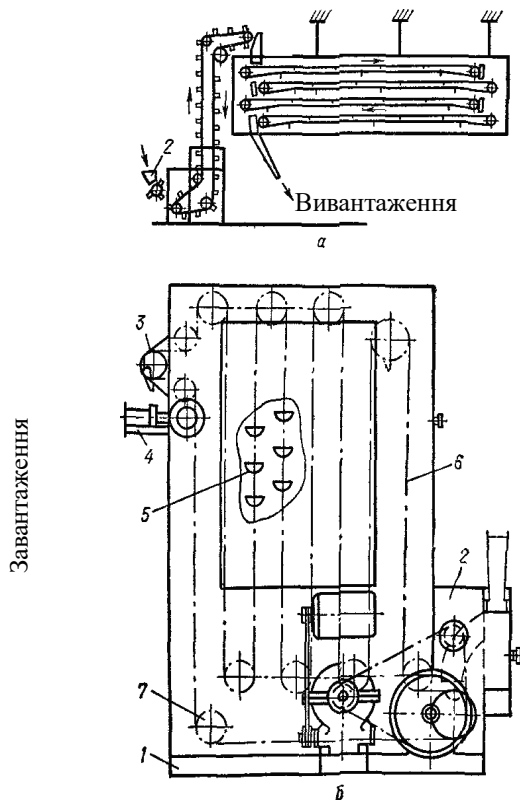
Шафи попереднього вистоювання: а – стрічкова; б – коліскова шафа; 1 – каркас; 2 – живильник; 3 – розвантажувальні зірочки; 4 – розвантажувальний поперечний конвеєр; 5 – коліски; 6 – ланцюговий конвеєр; 7 – зірочка.
